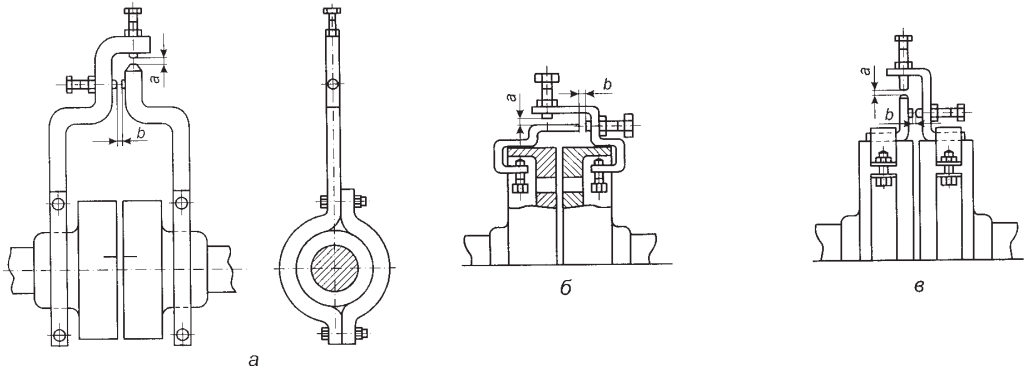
Скобы для центровки полумуфт: *а* — центровочные скобы; *б* — центровочные приспособления; *в* — центровочные приспособления с хомутами.
